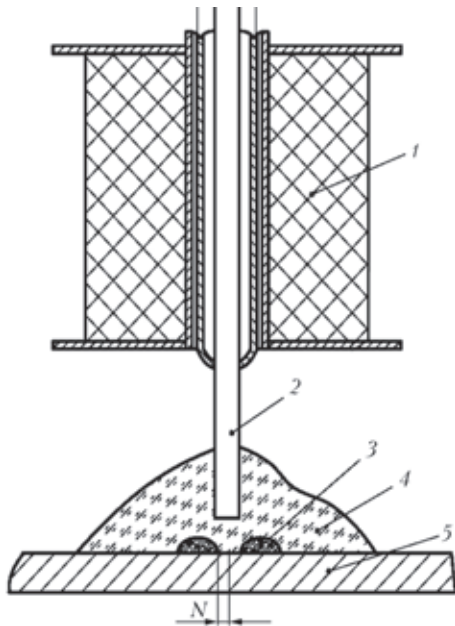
Схема автоматической дуговой наплавки под флюсом по легирующей шихте, расположенной вне зоны действия дуги, с наложением на дугу магнитного поля: 1 — катушка, создающая магнитное поле; 2 — проволока; 3 — слой легирующей шихты; 4 — флюс; 5 — наплавляемый образец; N — расстояние от центра дуги до слоя легирующей шихты
